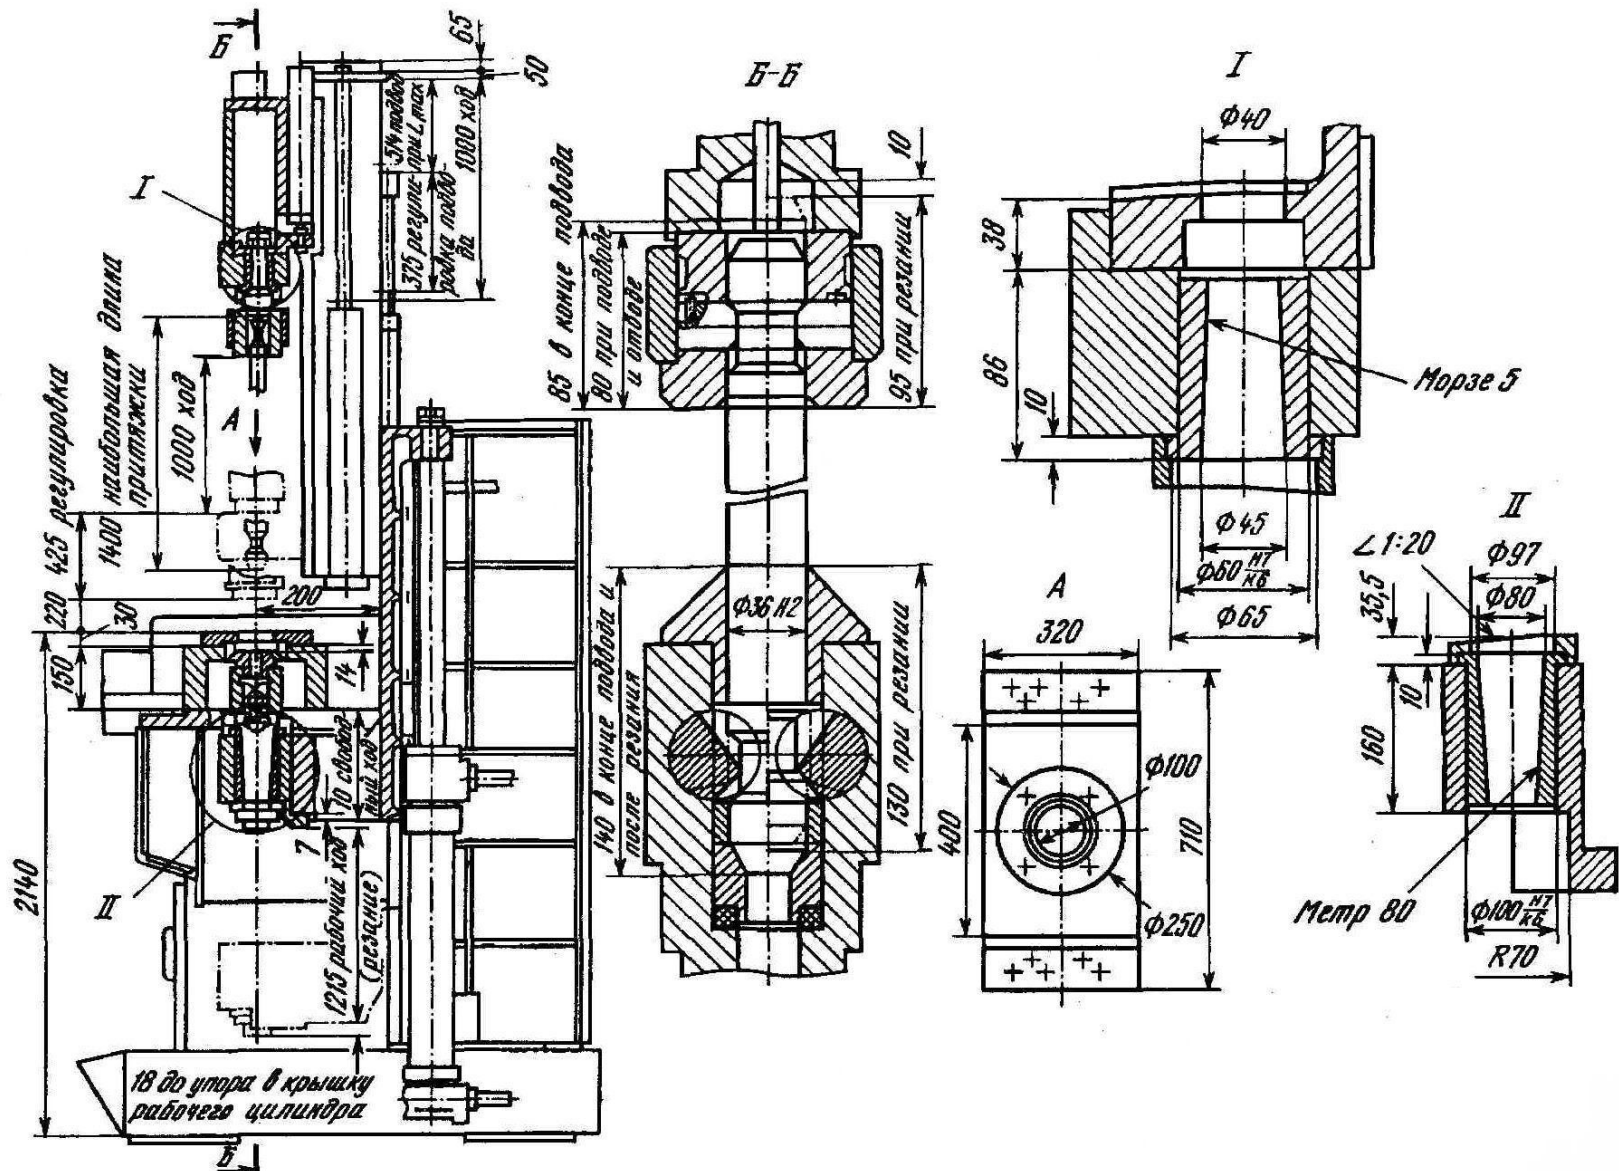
Схема наладки и присоединительные размеры вертикально-протяжного станка.
